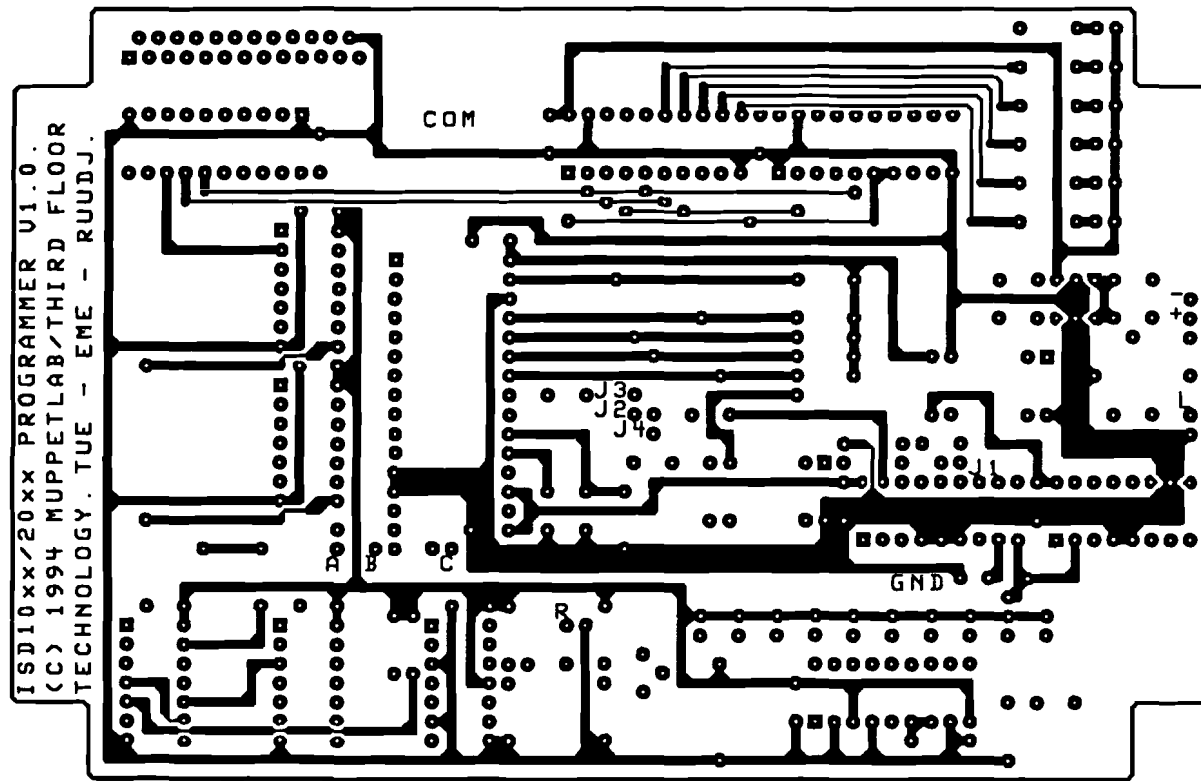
Printlayout van de ISD10xx/25xx programmer, component layer.
